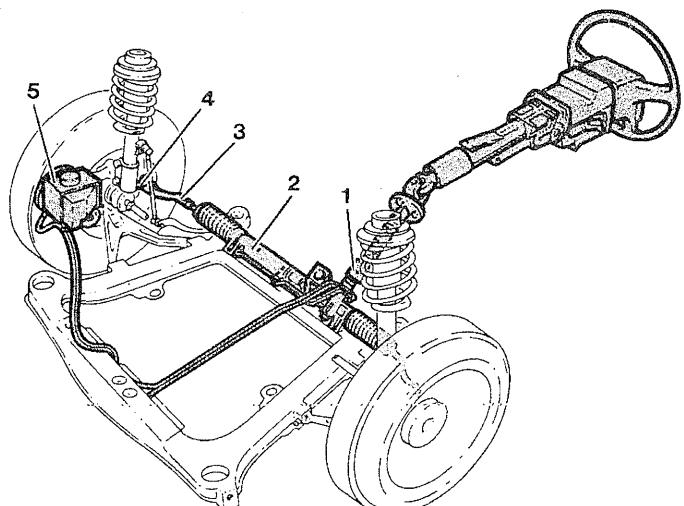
(1 — ось руля; 2 — редуктор рулевого механизма; 3 — продольная рулевая тяга; 4 — рычаг поворотного кулака; 5 — сервонасос с баком).
